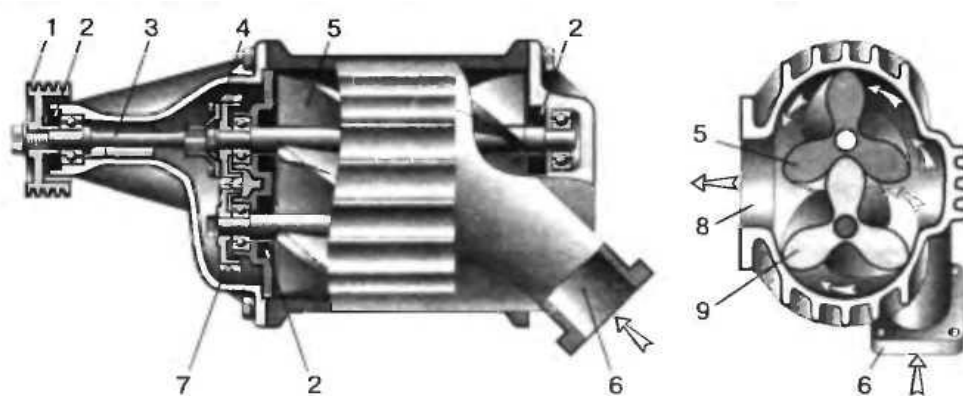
Схема приводного роторно-шестерного нагнітача: 1 - шків приводу; 2 - ущільнення; 3 - ресора; 4, 7 - синхронізуючі шестірни; 5, 9 - ведучий і відомий ротори; 6 - вхідний патрубок; 8 - вихід повітря у впускной колектор
